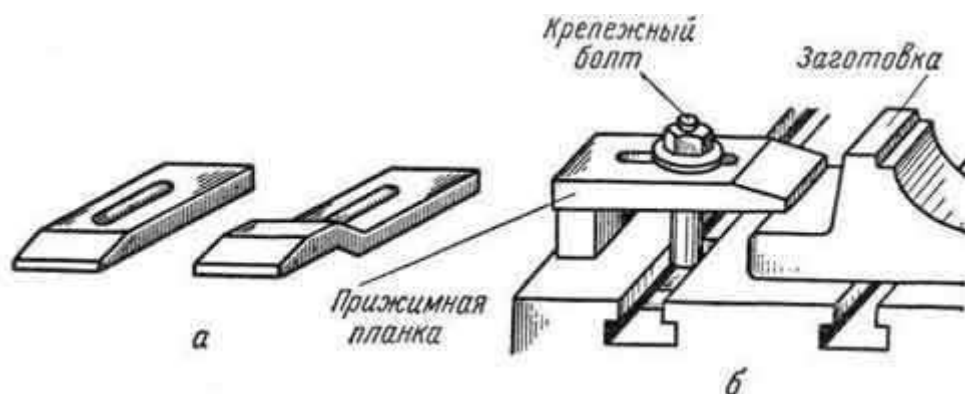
Прижимные планки (а) и способ крепления заготовки (б)
